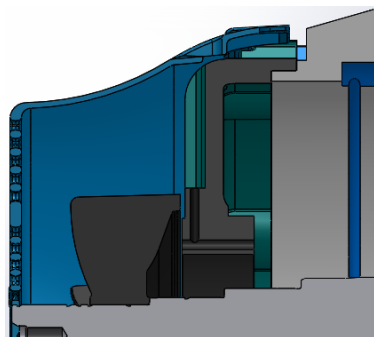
Posição 1 (Ventilador 295x114, Cota P=32mm, Cota H=5mm)
